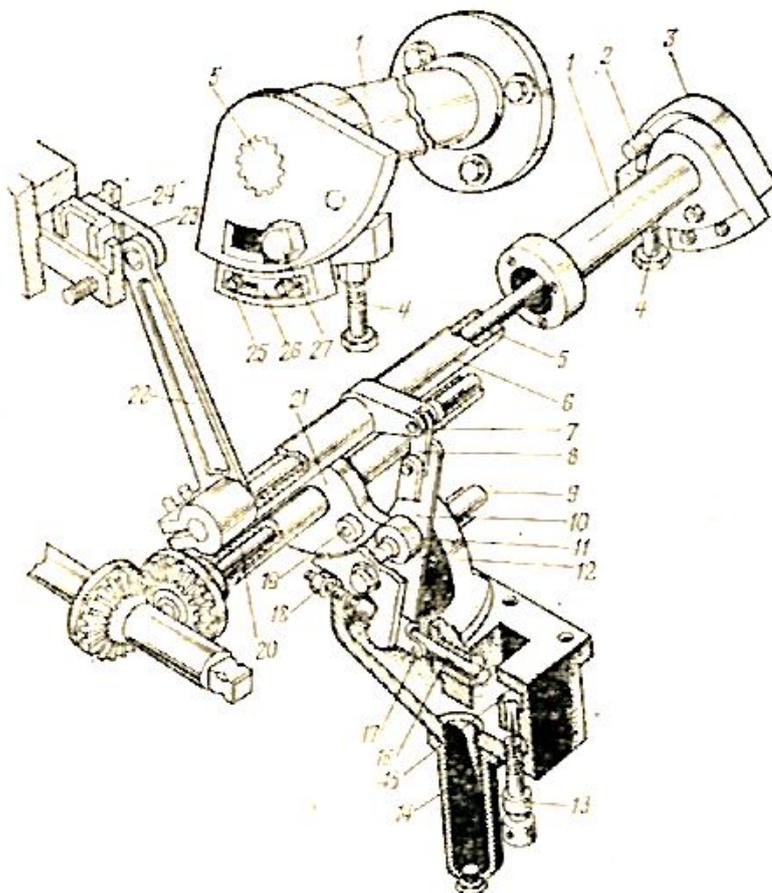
Боевой механизм: 1- кожух, 2-палец, 3- заводная муфта, 4- нажимной болт, 5- торсионный вал, 6- боевая труба, 7- палец шарнира, 8- проушина шарнирного звена, 9-ось трехплечего рычага, 10-трехплечий рычаг, 11- ролик, 12- ось ролика, 13- регулировочная игла, 14- корпус отстойника. 15- цилиндр, 16- поршень, 17- шатун, 18-регулировочный, винт, 19- спусковые ролики, 20- поперечный вал, 21- боевой эксцентрик, 22-подгонялка, 23- серьга, 24- гонок, 25-винты, 26- шкала, 27- болт.
